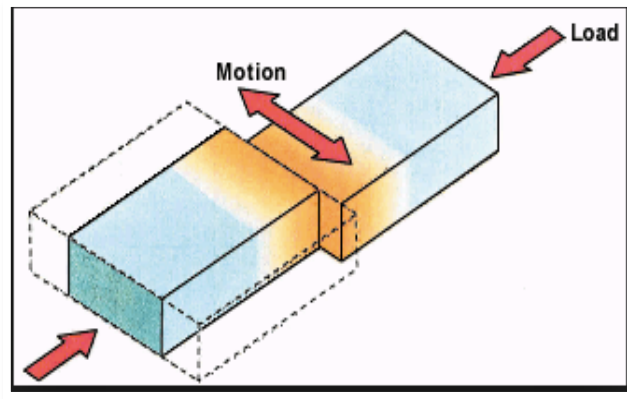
principe de soudage par friction linéaire [25].
